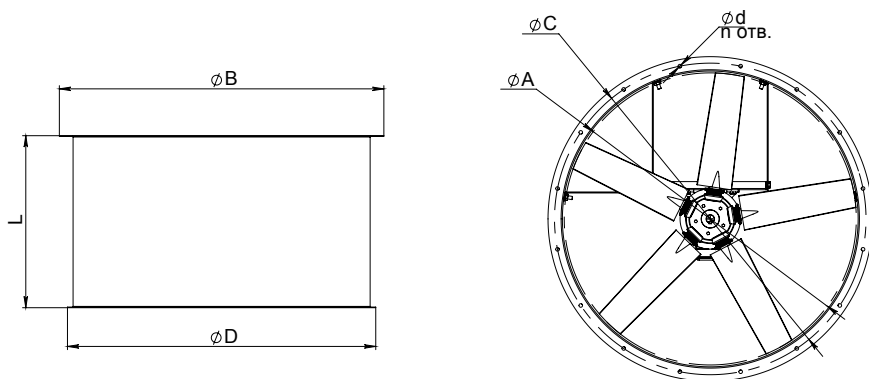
Габаритные размеры вентилятора в исполнениях корпуса «VI» и «V0»
